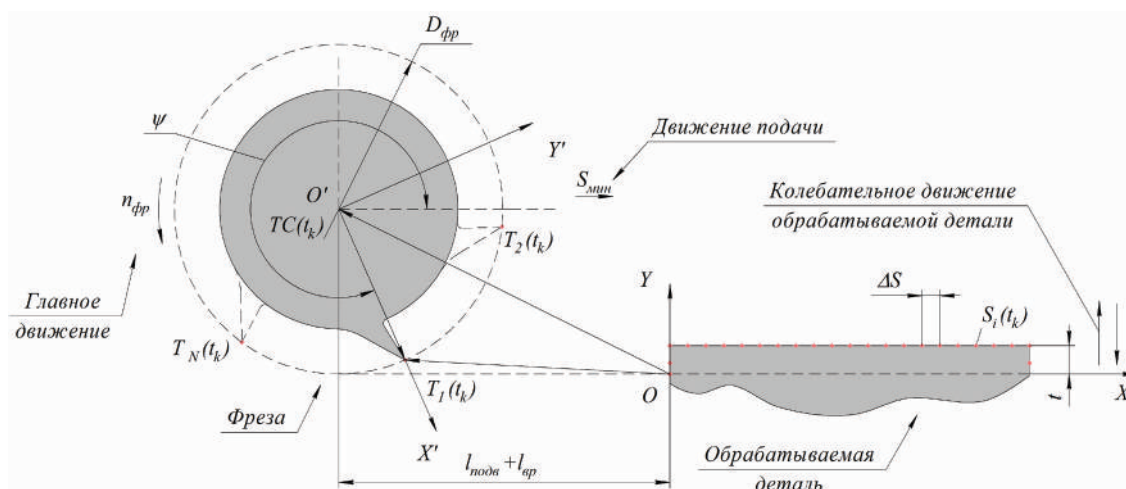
Геометрические модели фрезы и обрабатываемой детали
